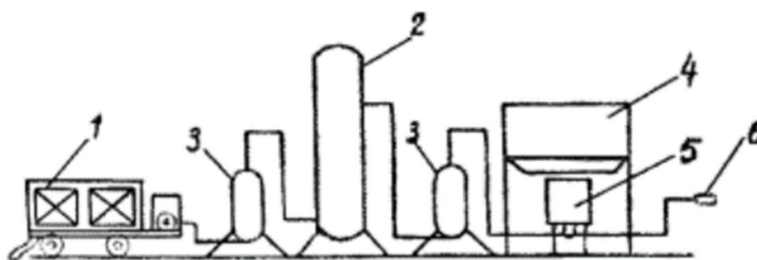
Схема пескоструйной установки: 1 – компрессор; 2 – ресивер; 3 – маслоотделитель; 4 – загрузочный бункер с песком; 5 – пескоструйный аппарат; 6 – пистолет-распылитель с соплом
